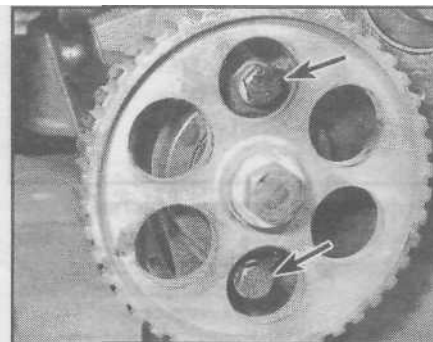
, а. Болты крепления фланца промежуточного вала (показаны стрелками)
